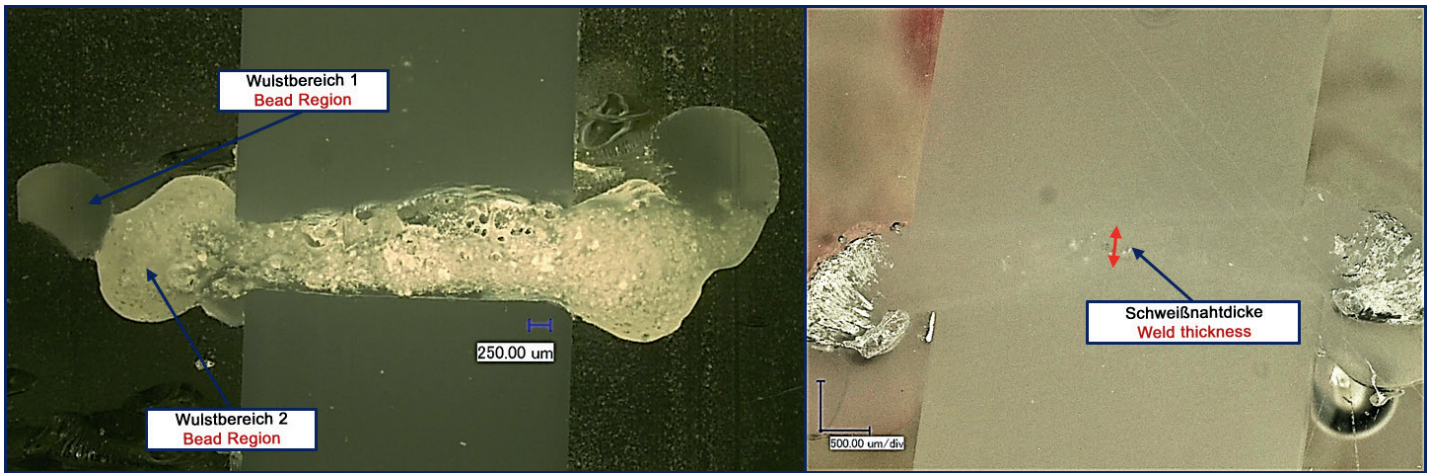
Mikroskopische Aufnahmen der Schweißnähte bei variierender initialer Schmelzeschichtdicke (links: 0,3 mm; rechts: 1,0 mm)
